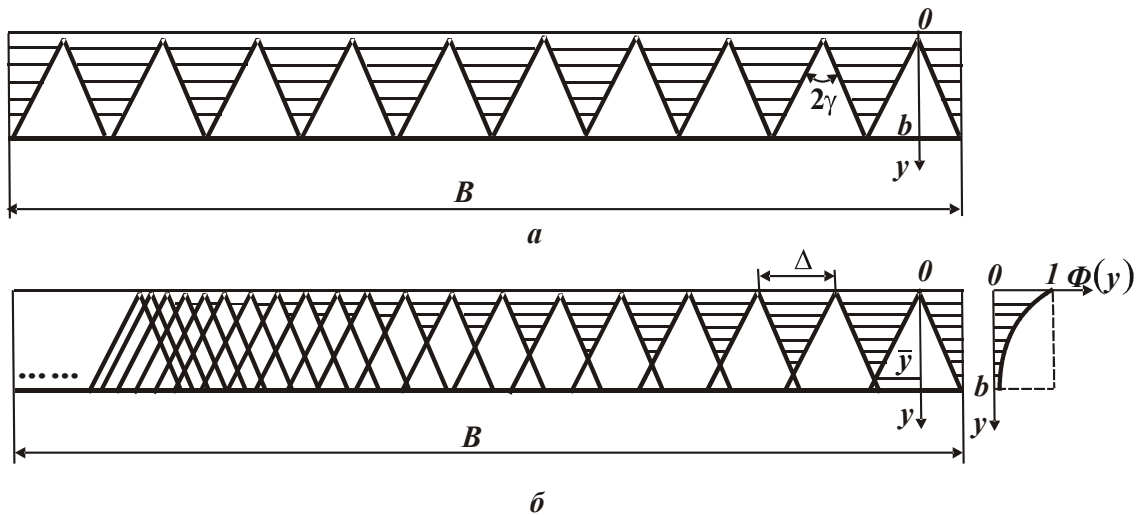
Схемы формирования шероховатости поверхности при абразивной обработке
